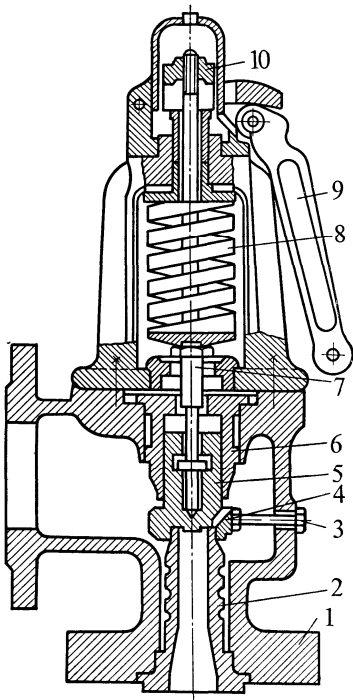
Пружинний запобіжний клапан, розрахований на тиск 12,5 МПа 1 - корпус; 2 - втулка (сідло); 3 - упорний закріплюючий штифт; 4 - кільце, що напружає (регулює); 5 - тарелка клапана; 6 - направляюча втулка; 7 - шток; 8 - пружина; 9 - пристрій для підриву клапану від руки; 10 - гайка для регулювання клапану.
